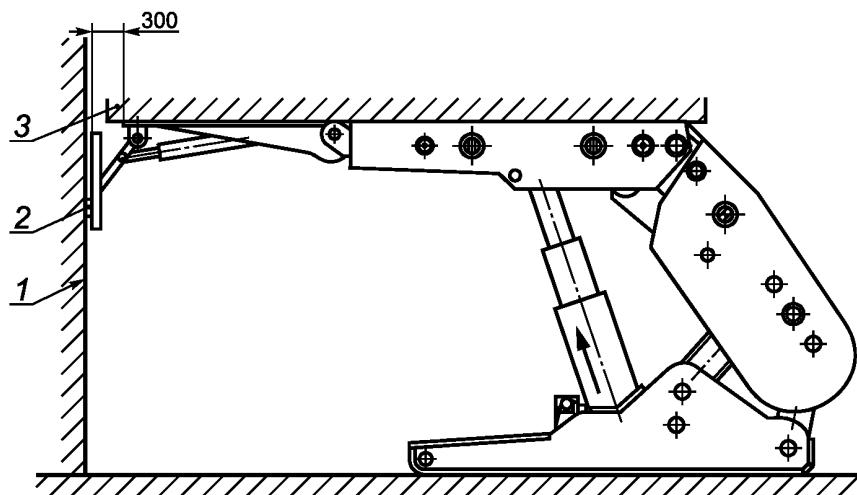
Схемы испытаний перекрытий и оснований на выпучивание опор
